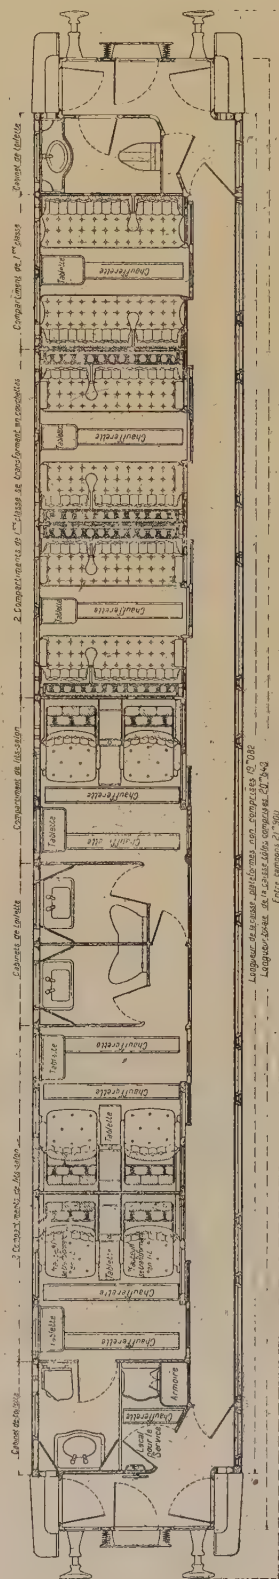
Plan de la voiture A3013gyll, du P.-L.-M.
